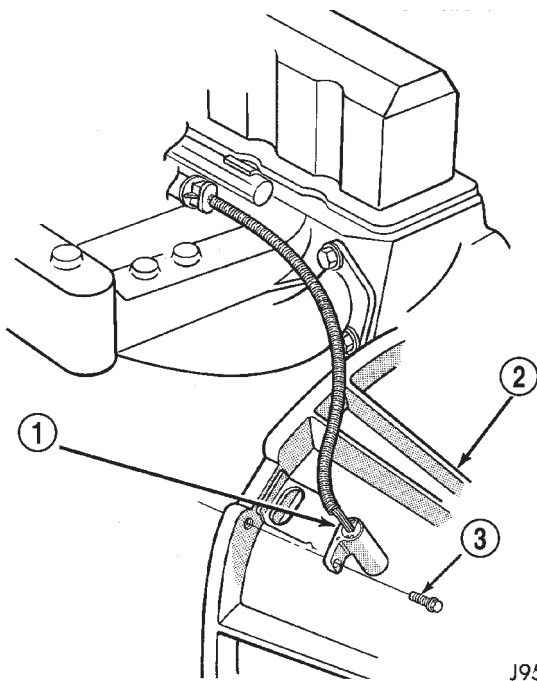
Sensor de posición del cigüeñal - Motor 4.0L
